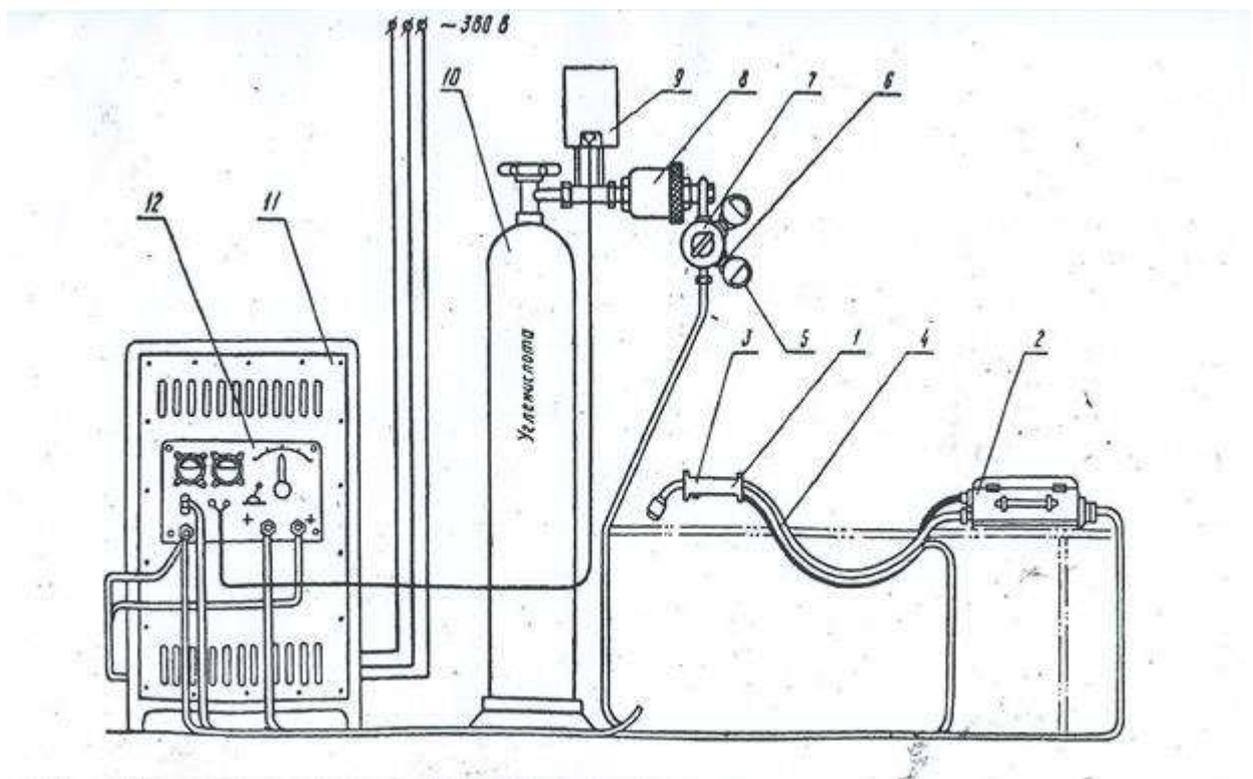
Схема (общий вид) полуавтоматической установки для сварки тонкой электродной проволокой в среде углекислого газа " (1 - держатель, 2 - механизм подачи проволоки, 3-кнопка включения, 4 - шланг, 5 - ацетиленовый манометр на 6 ат, 6 - переходной штуцер ацетиленового манометра, 7 - кислородный редуктор, 8 - осушитель)
